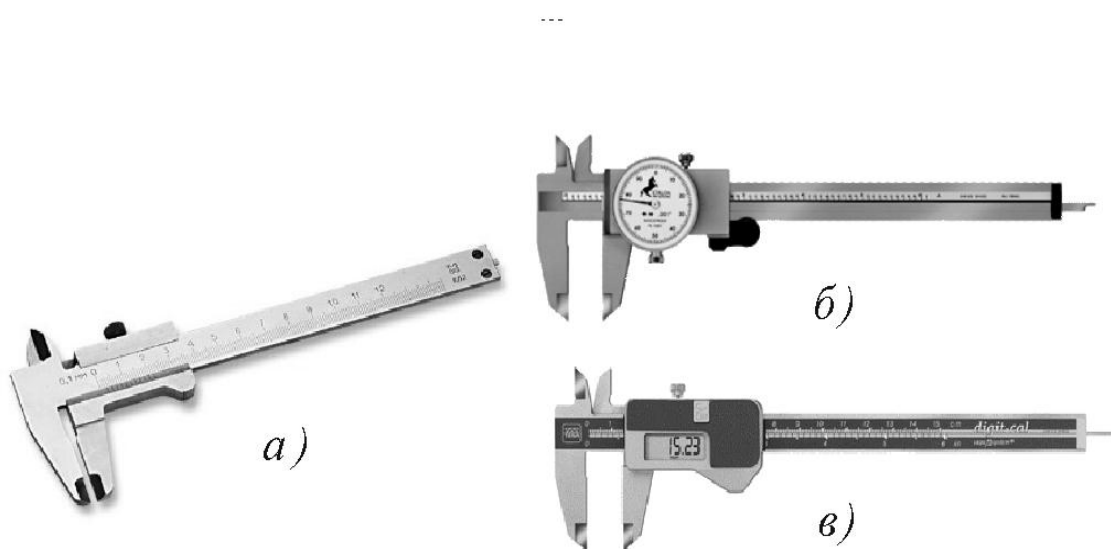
Модели штангенциркулей: а) нониусный; б) индикаторный; в) цифровой
